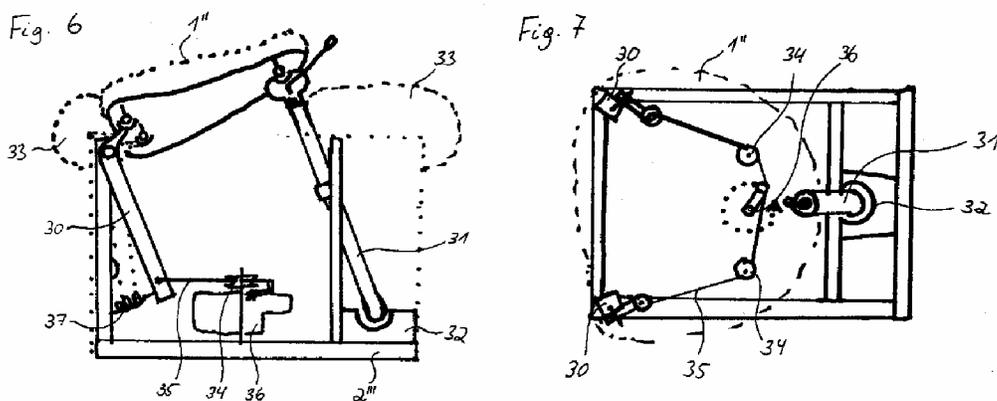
Antriebsmodul Gangbild Pferd, links Seitenansicht (Fig. 6), rechts Draufsicht (Fig. 7)
